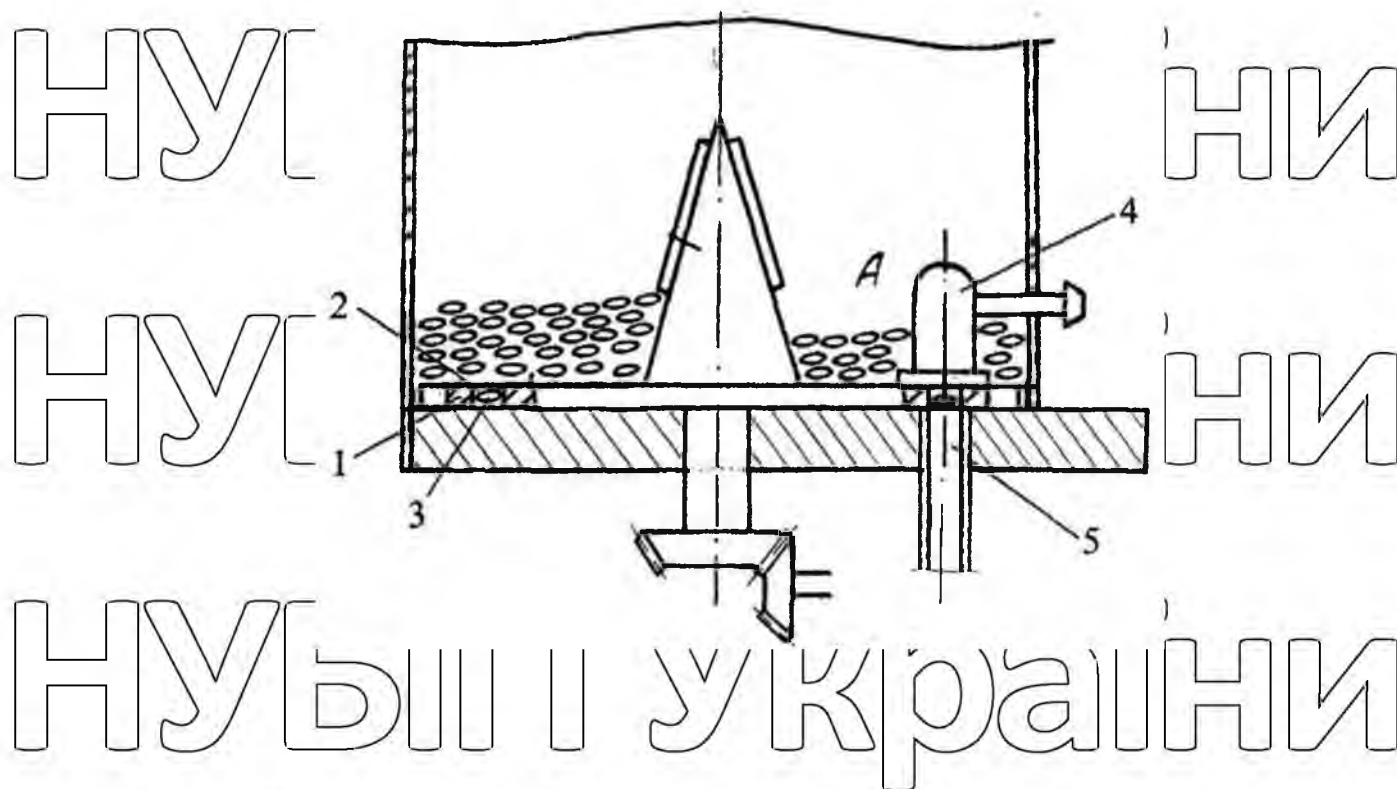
Принципова схема дискового пневмомеханічного апарата
